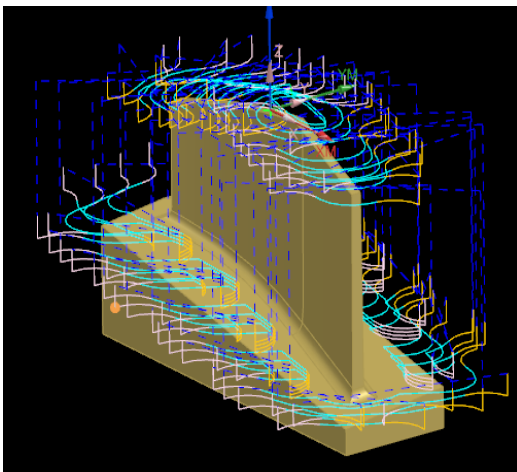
Žebrová elektroda– dráhy před změnou (hrubování) [autor]
